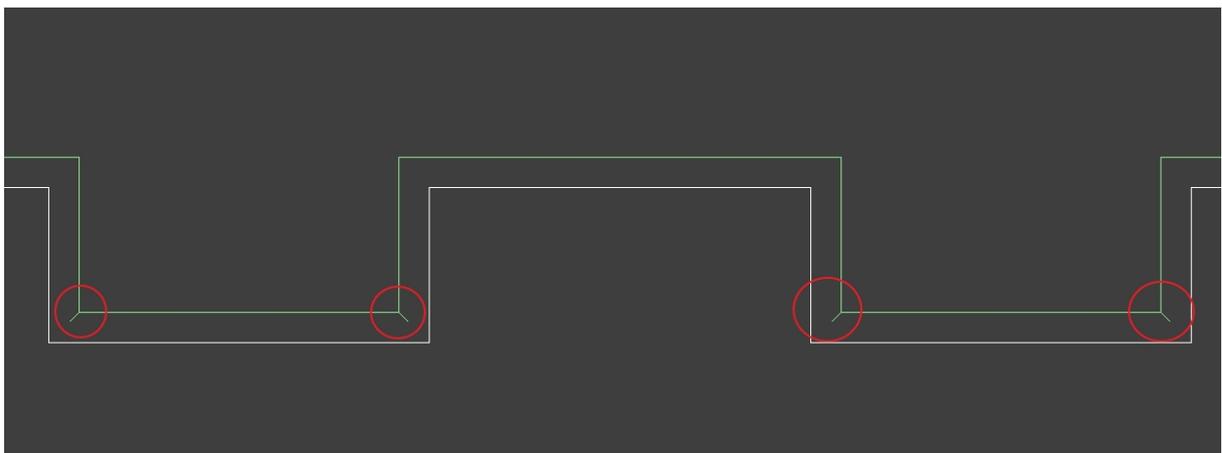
Die Wirkung in der Anzeige des Werkzeugpfades
